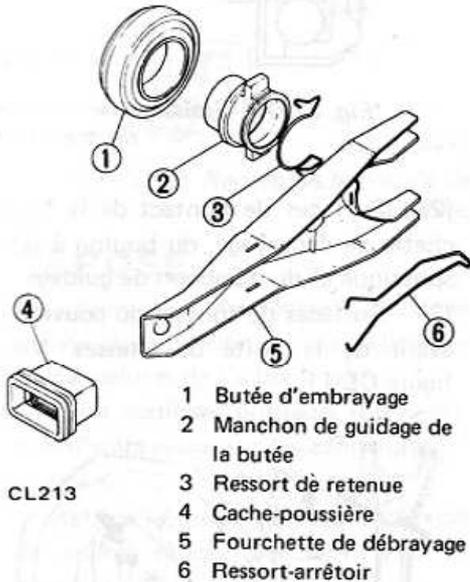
Vue éclatée du mécanisme de débrayage
